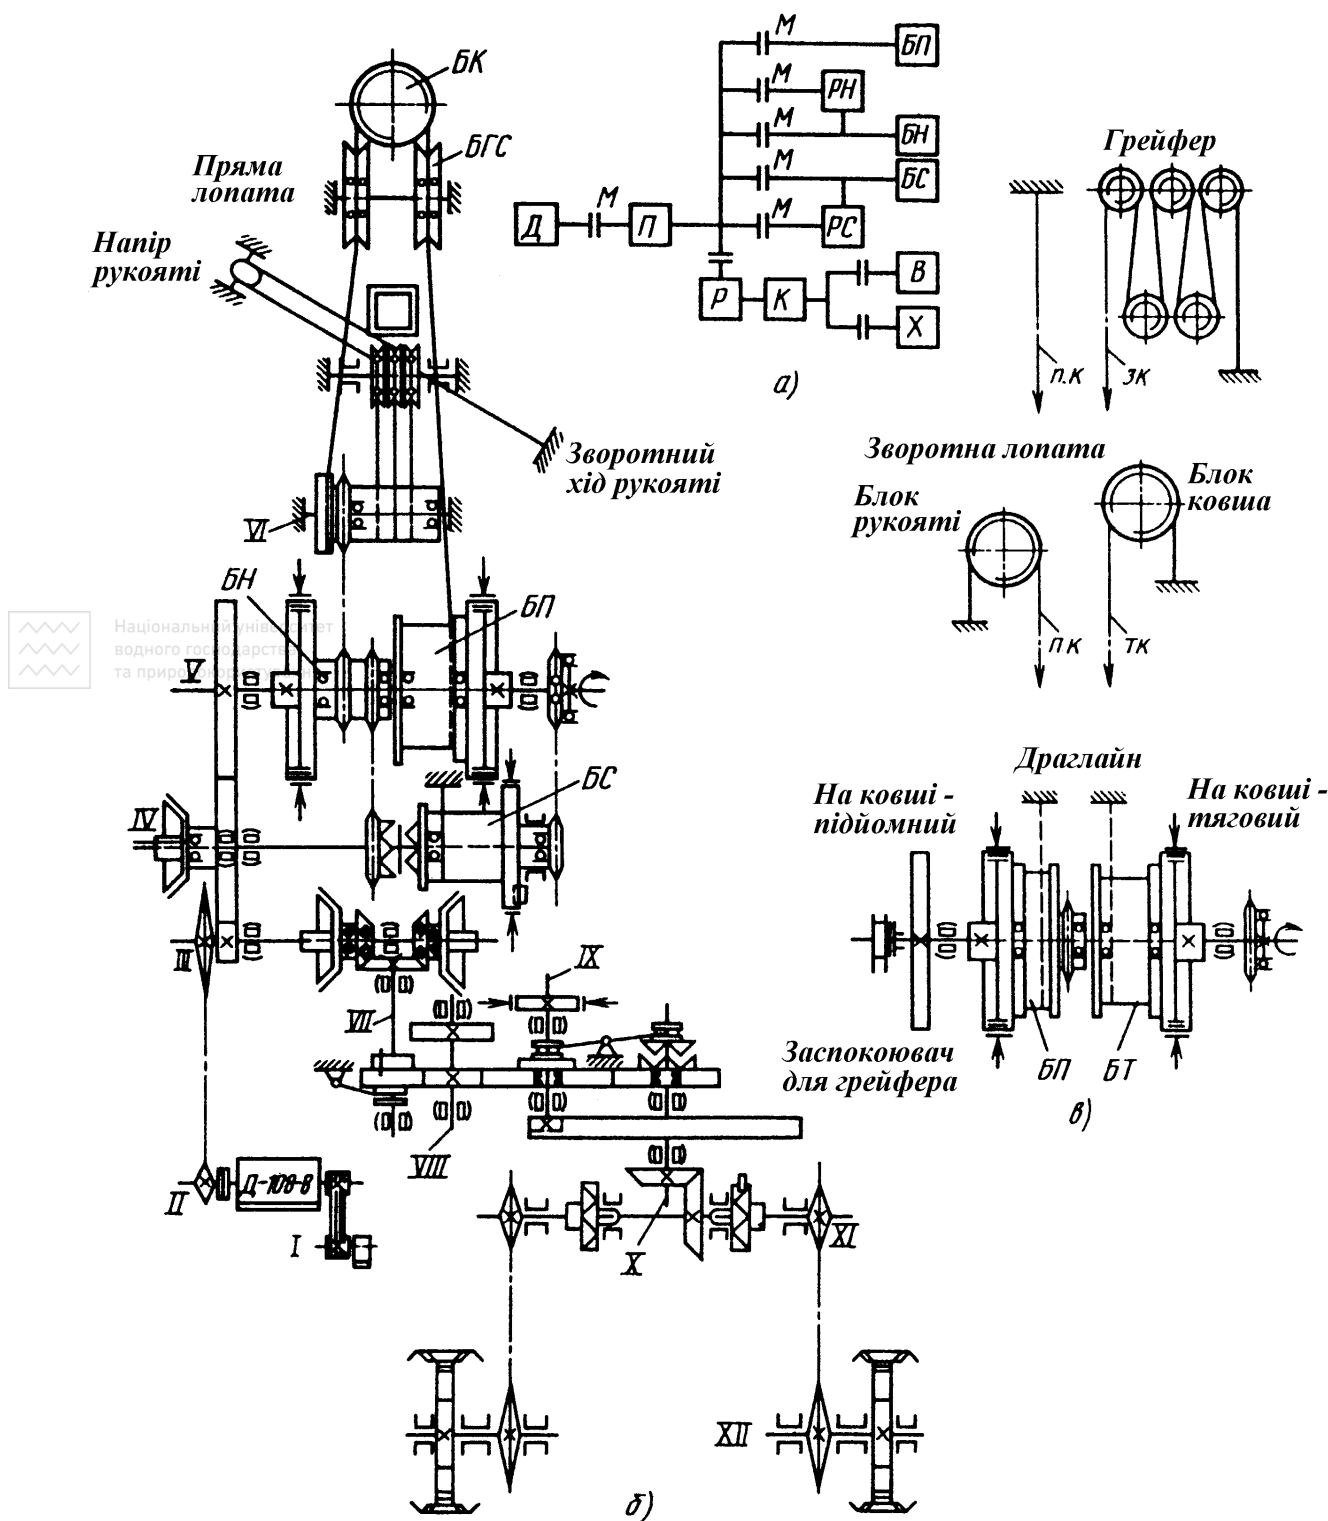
Структурна а) і кінематична б) схеми і схеми запасування канатів в) екскаватора ЕО-4111В: БП - барабан лебідки підйому ковша; БГС - блок голови стріли; БК - блок ковша; БН - напірний барабан; БС - барабан лебідки підйому стріли; I-XII - вали механізмів
